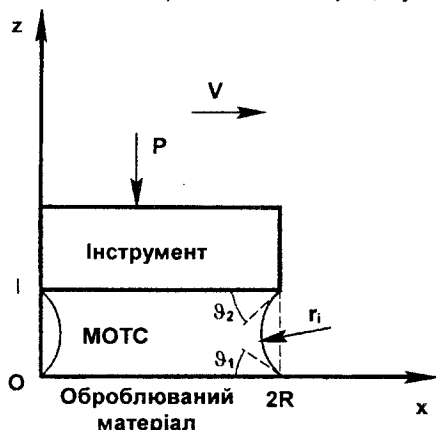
Схема контакту поверхонь інструменту та оброблюваної деталі в нерівноважному процесі полірування
